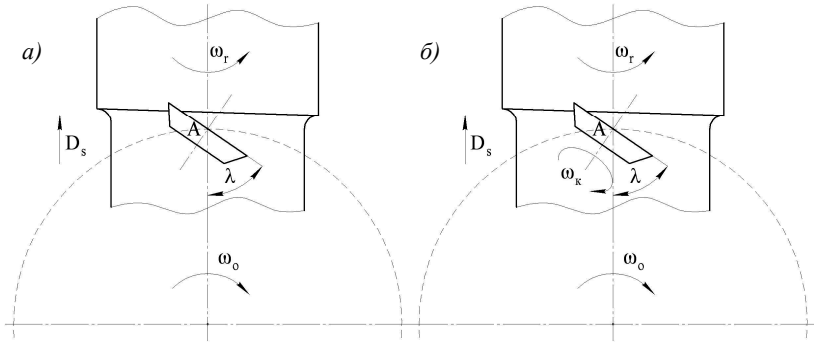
Резание заготовки торцовой (а) и ротационной (б) фрезями
